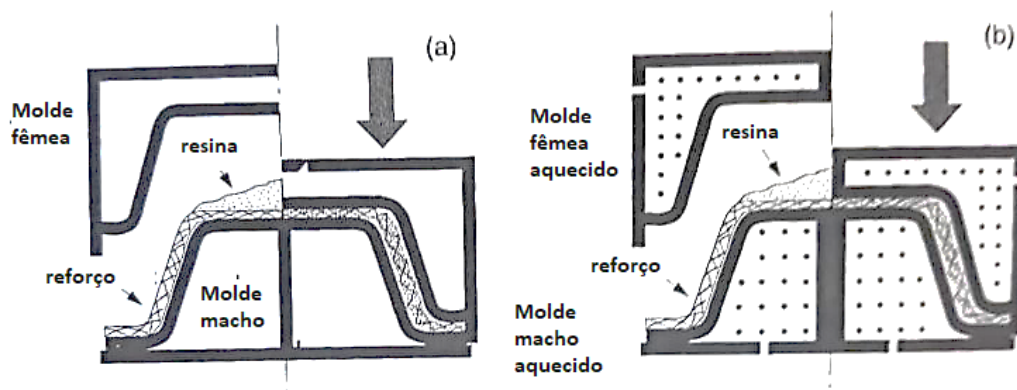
Esquema de moldação por compressão a frio (a) e moldação por compressão a quente (b). Adaptado de [63].
